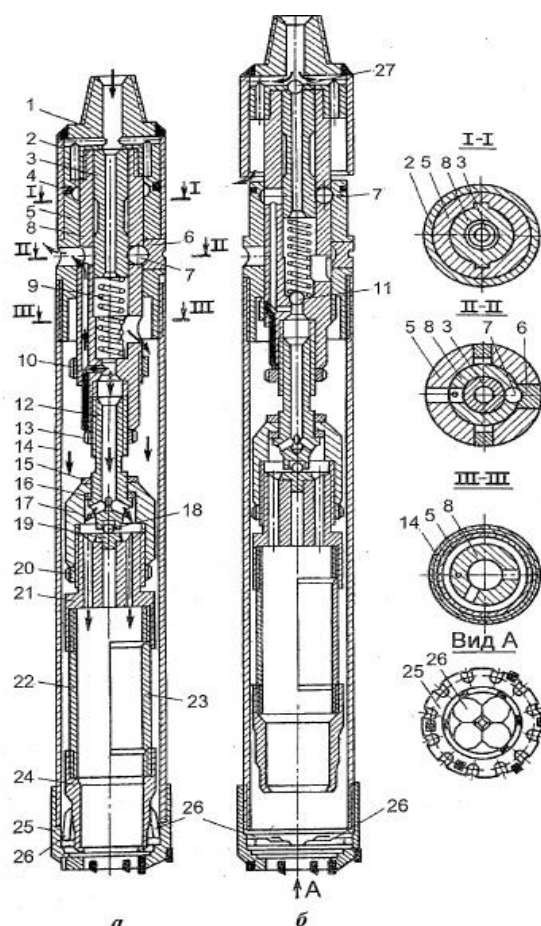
Универсальный двойной колонковый снаряд конструкции Томского политехнического института (ДКС-У-ТПИ): 1 – переходник; 2 – кожух; 3 – золотник; 4 – сальник; 5 – корпус; 6 – пробка; 7 – шарик-фиксатор; 8 – шпindelь; 9 – пружина замкового механизма; 10, 13 – котргайки; 11 – шаровой клапан; 12 – регулировочный винт подвески; 14 – наружная колонковая труба; 15 – уплотнительная прокладка (сальник); 16 – шайба (подшипник); 17 – корпус узла подвески; 18 – опорный шарик (подшипник); 19 – подпятник; 20 – контргайка; 21 – головка керноприемника; 22, 23 – разрезной керноприемник; 24 – стакан; 25 – коронка; 26 – кернорвательные пластины (клапаны); 27 – шаровой клапан
